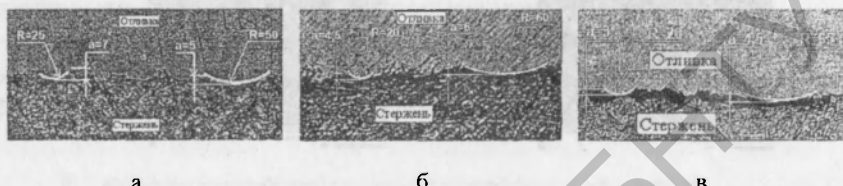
Схема образования зон возможного взаимного пересечения профилей и свободных зон (зазоров) при перемещении отливки относительно стержня (фрагмент)
